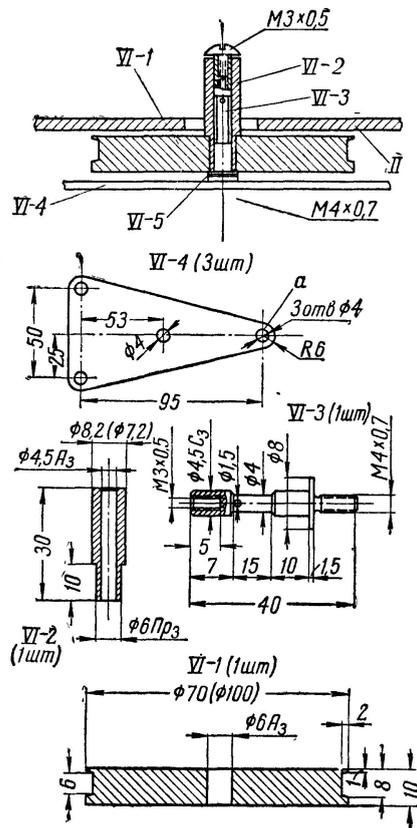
Сборочный чертеж и детали ведущего узла. VI-1 — маховик — материал сталь или бронза; VI-2 — ведущая втулка — материал бронза. После запрессовки в дет. VI-1 установить в станок на оправке и проточить до наружного диаметра 8 мм. Радиальное биение ведущей втулки и маховика относительно оси не должно быть более 0,02; VI-3 — ось — материал ЗОХГСА или какая-либо другая; VI-4 — пластина материал Д16Т — Л2,5 можно заменить сталью, текстолитом; VI-5 — шайба из гетинакса или текстолита.
